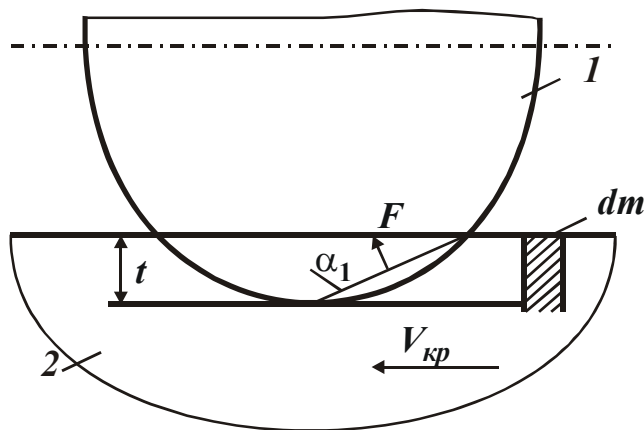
Расчетная схема: 1 – обрабатываемая деталь, 2 – рабочая поверхность круга.
